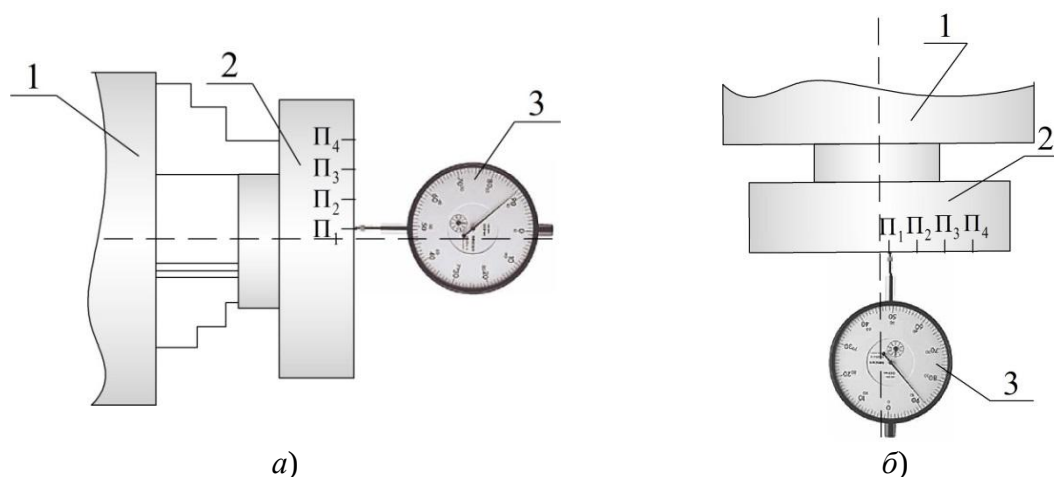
Схема контроля торцового биения: *а* – шпинделя токарного станка; *б* – шпинделя вертикально-фрезерного станка
